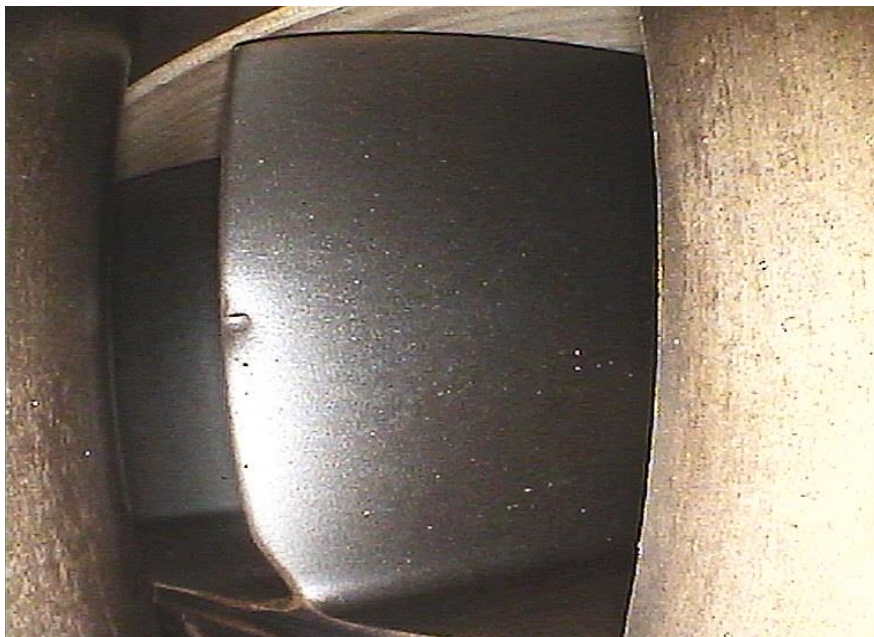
Вмятина на выходной кромке рабочей лопатки 14 ступени компрессора глубиной до 1 мм
